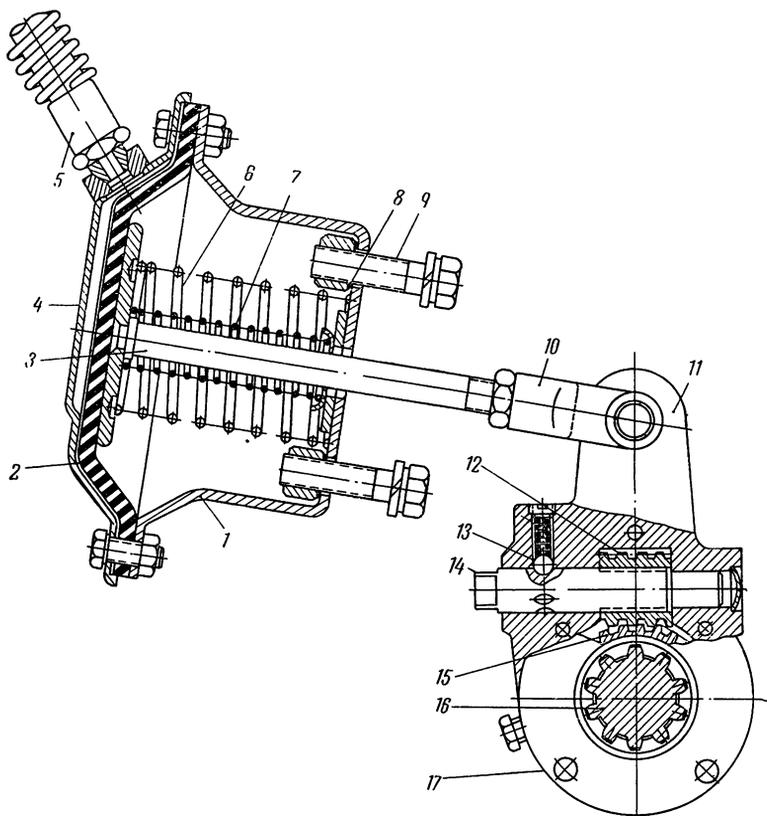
Тормозная камера с регулировочным рычагом в сборе:
